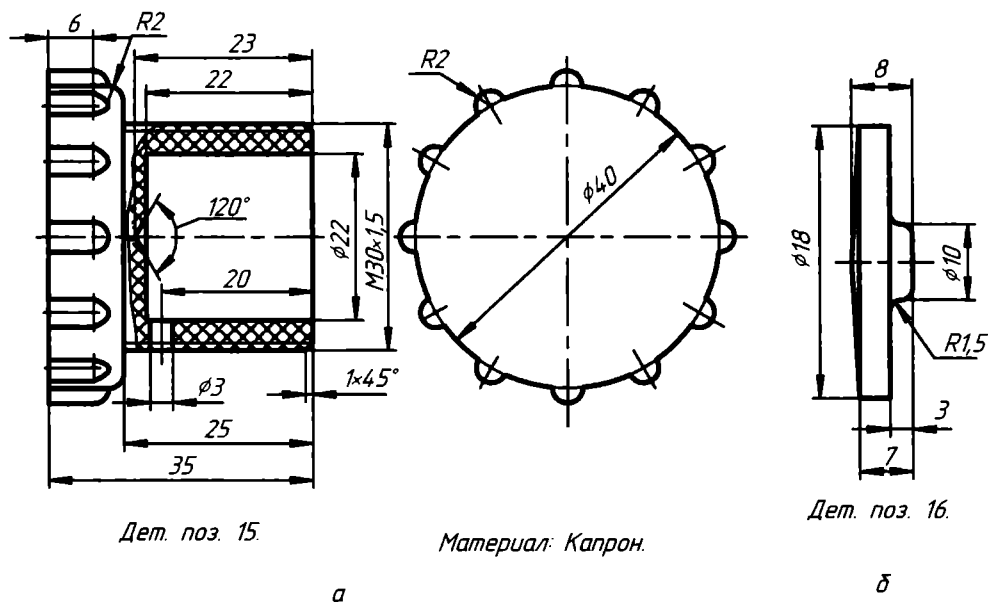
Чертежи: а — втулки; б — опоры пружины
